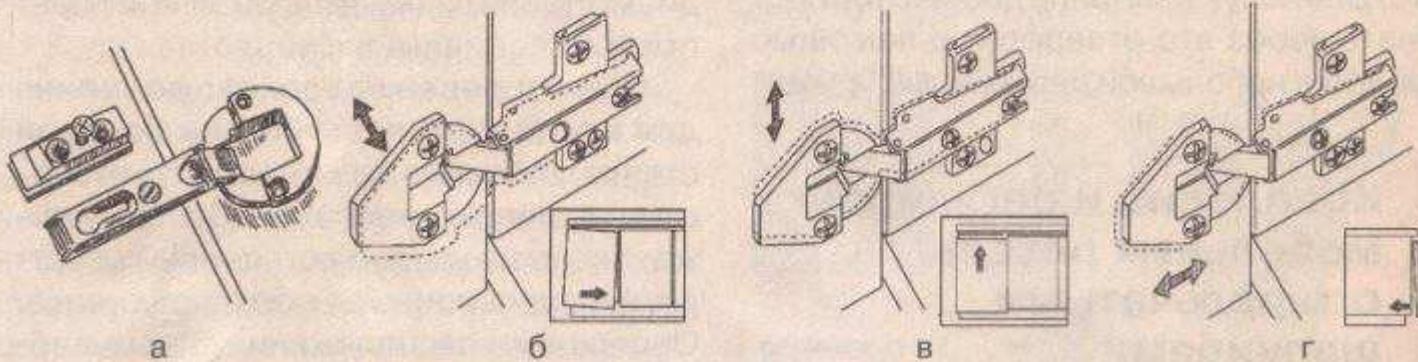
Выравнивание дверцы: а — петля с обычной регулировкой и петля с механизмом регулировки при помощи среднего винта; б — боковая регулировка; в — регулировка по высоте; г — регулировка по глубине; 1 — регулирующий винт
